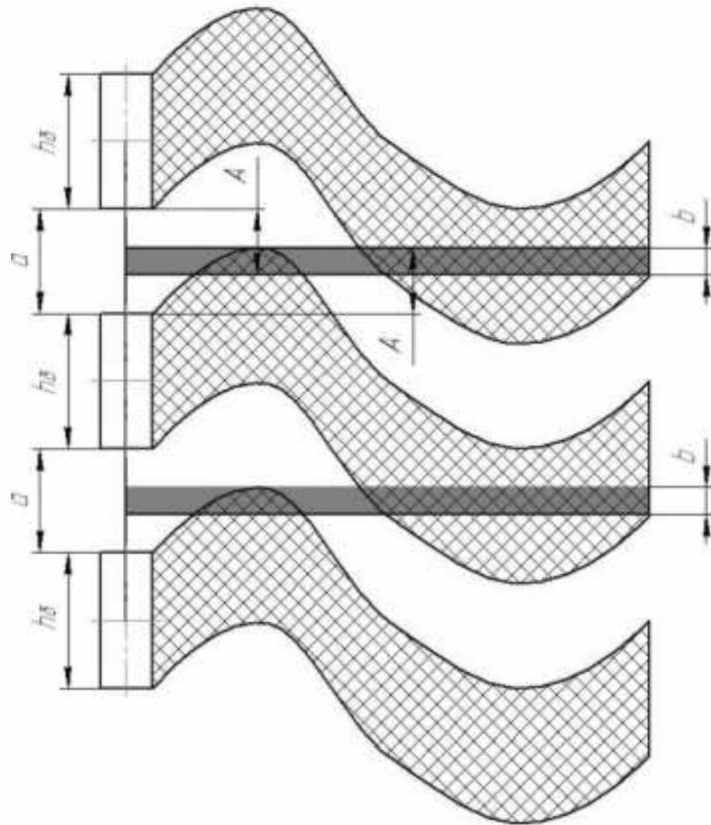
Схема кінематичного контакту інструментальних брусків в головці ГКО для відновлення внутрішньої циліндричної поверхні
